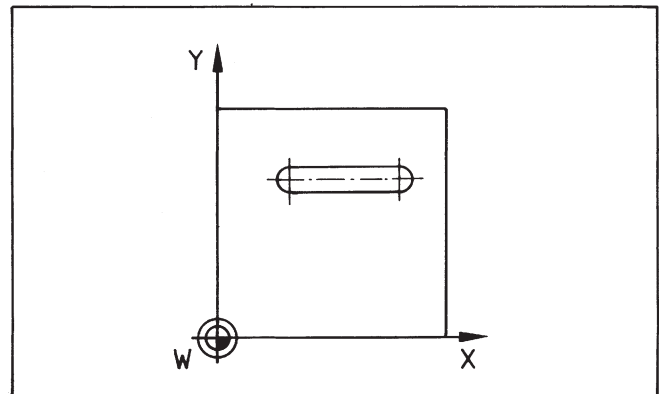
Wahl des Werkstücknullpunkts bei der Senkrecht-Werkzeugfräsmaschine MF1
